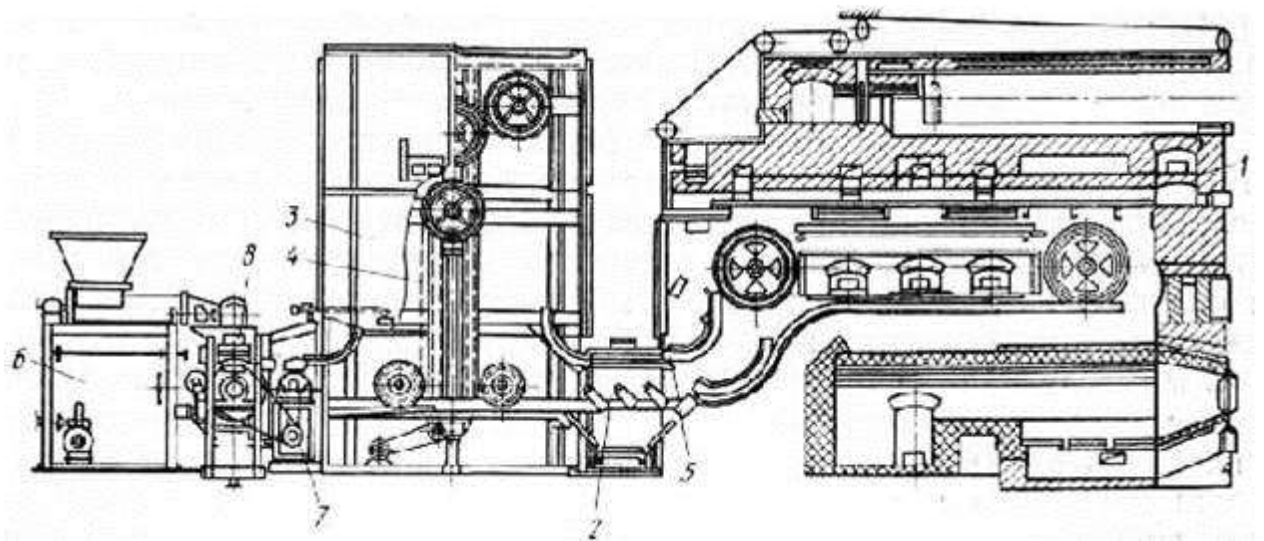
Розстойно-пічний агрегат Р-2-59м:
